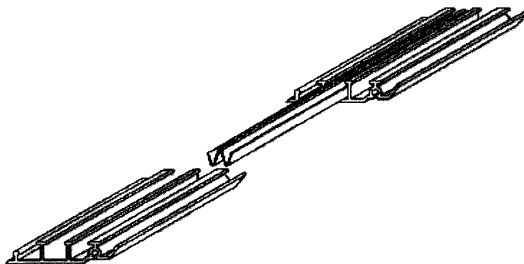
Подготовка ПВХ-профиля к сращиванию
